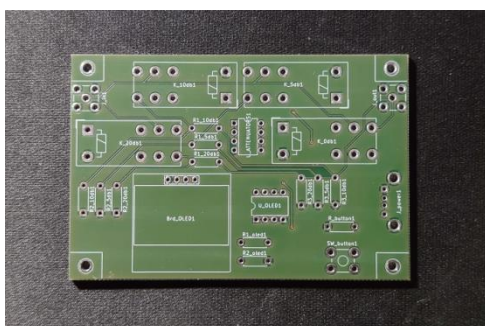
PCB πλακέτα 3D (front)
